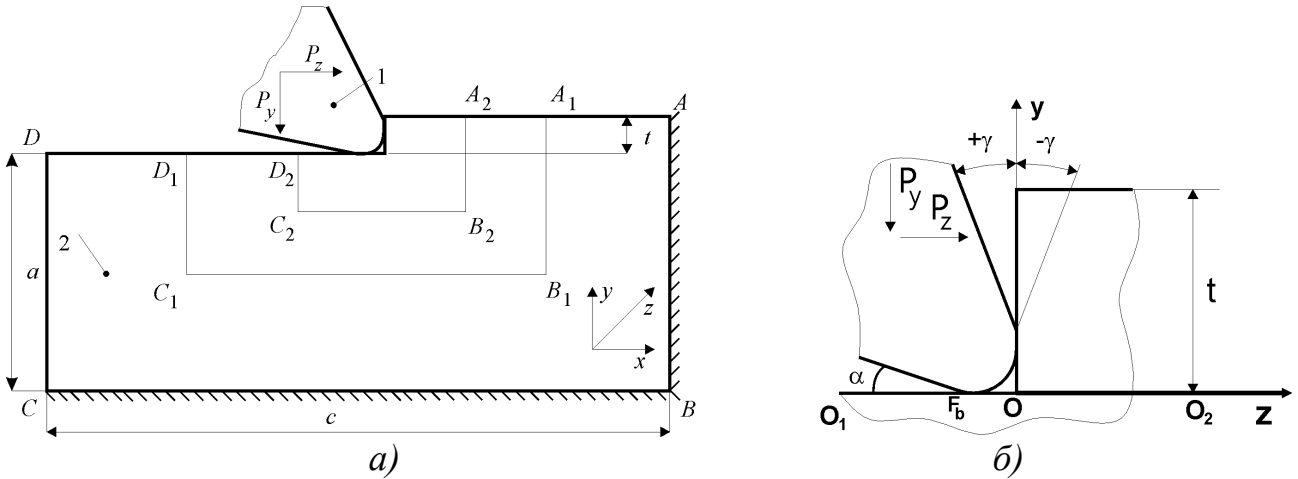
Розрахункова схема задачі визначення НДС ПКМ: а – загальна розрахункова схема; б – схема контактної взаємодії вершини інструменту і матеріалу
